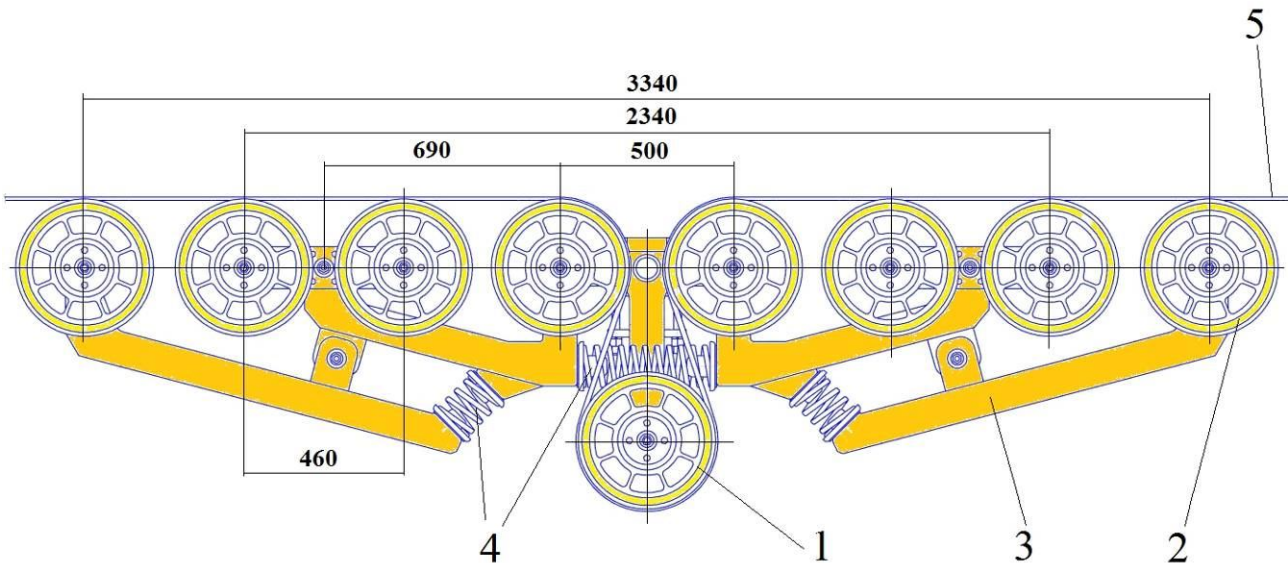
Конструкция мехатронного модуля гибкого тягового (приводного) каната [4]: 1 – приводное колесо; 2 – направляющий каток; 3 – балансир; 4 – демпфер; 5 – тяговый канат
